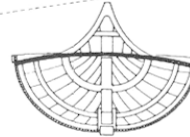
Plan et élévation de l'assemblage du fond avec la quille
